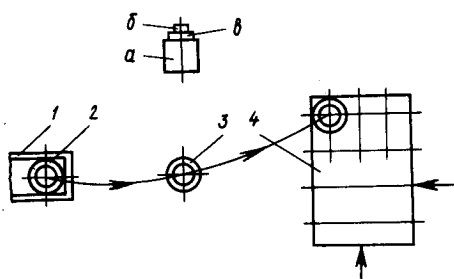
Схема работы кассеты для питания робота: а — база для ориентации в лотке вибробункера и в кассете; б — база для захвата рабочим органом робота; в — база для сборки с сопряженной деталью; 1 — лоток вибробункера; 2 — деталь; 3 — сборочная позиция; 4 — кассета собранных узлов
